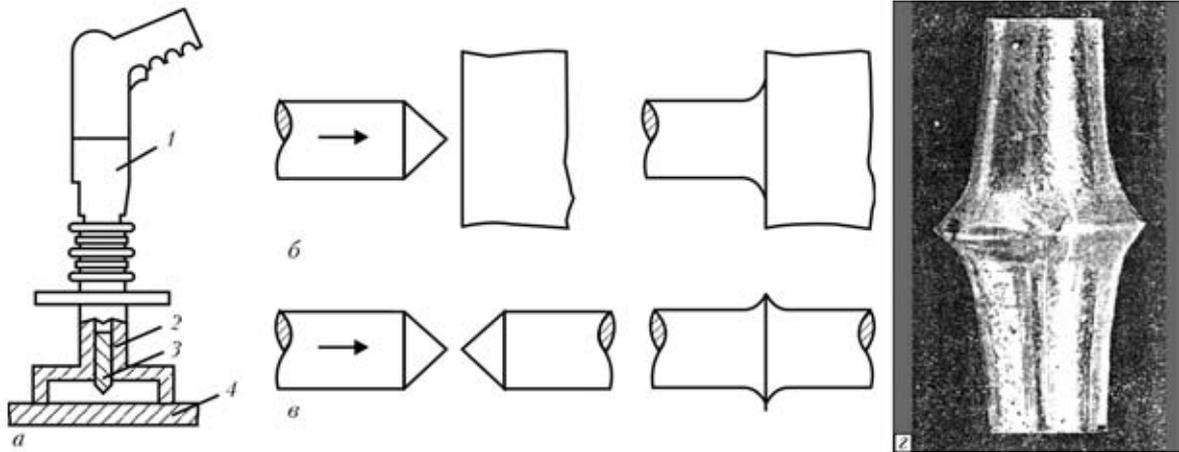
Схема переносного устройства (пистолета) для СВУ шпилек (а), схемы процесса сварки шпилек с основанием (б) и между собой (в): 1 — пистолет-ускоритель шпилек; 2 — защитный чехол; 3 — шпилька; 4 — основание для приварки шпилек; z — фотография сваренных встык медных шпилек диаметром 9,5 мм [7]
